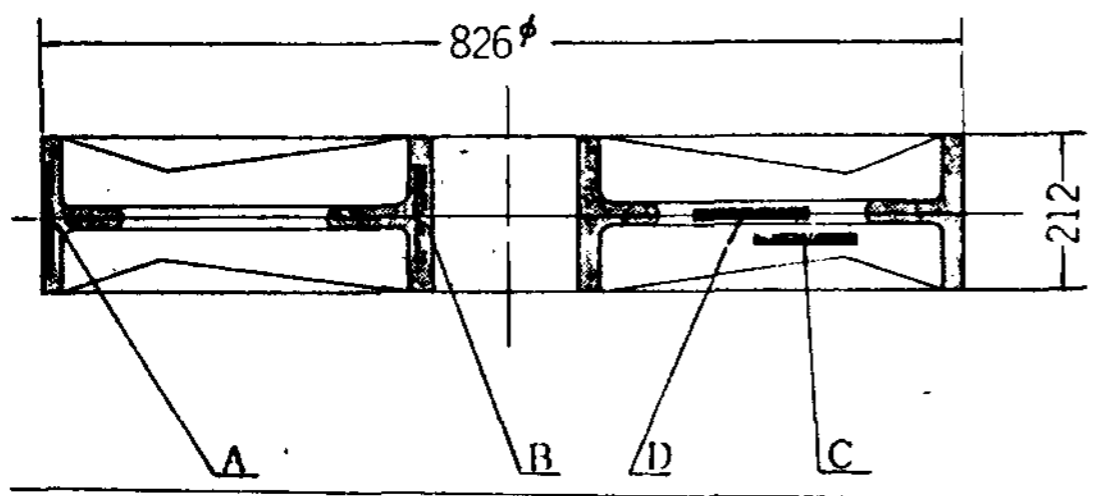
Rod Wheel 實體 試驗片 彩取位置 (mm)
